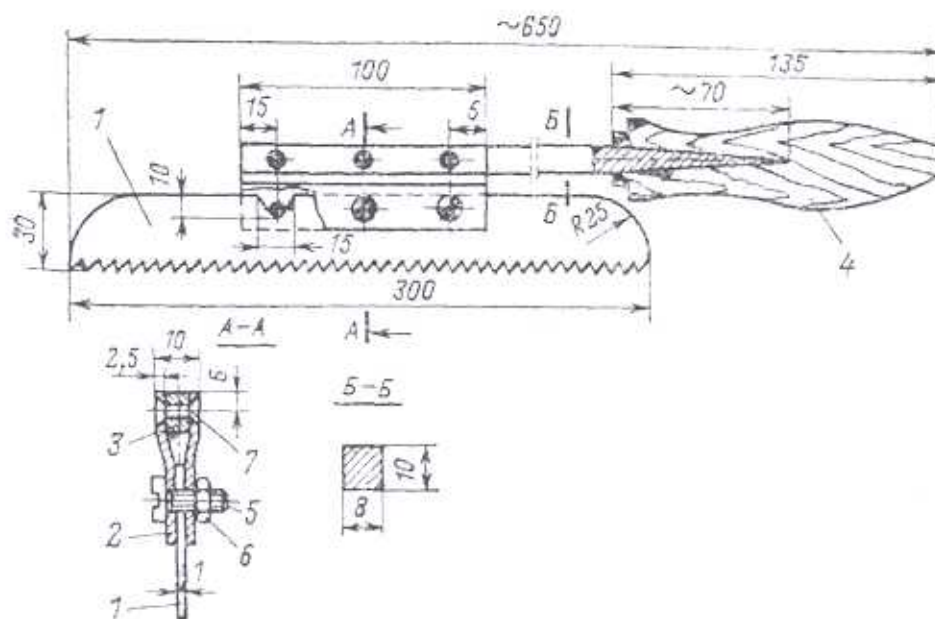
Приспособление для обрезки вентиляционных трубок (ТГВ):
